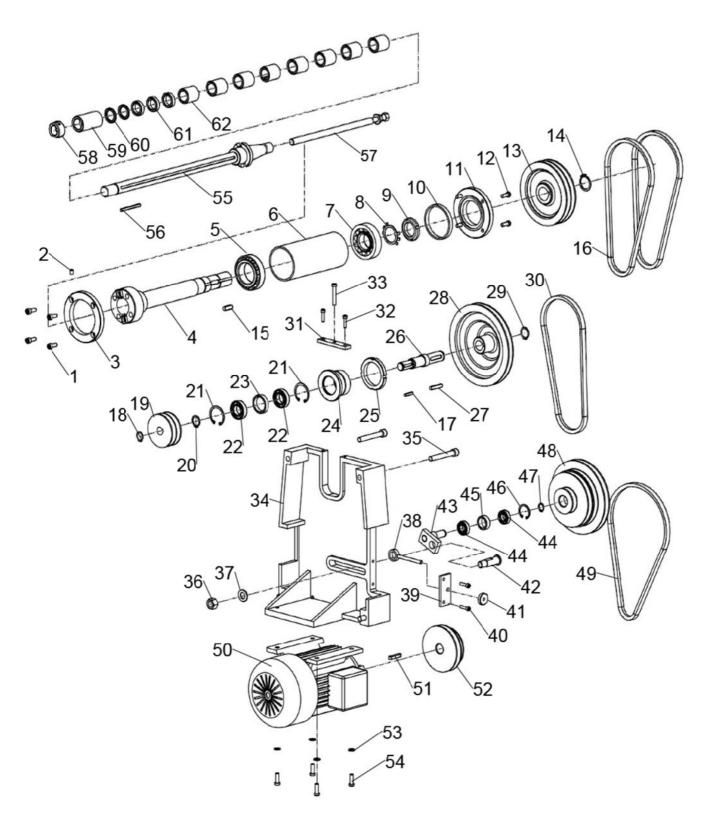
Riementrieb Horizontalfräsen - Belt drive horizontal milling
